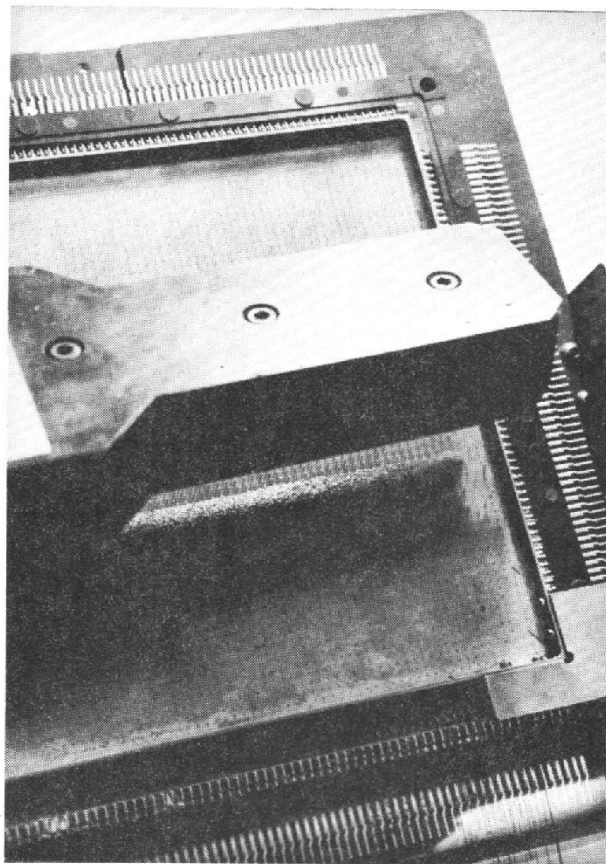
La mémoire à aiguilles est fabriquée entièrement automatiquement. L'utilisation d'un champ magnétique permet à des milliers d'aiguilles de se dresser sur la pointe et de « marcher » sur le plan de mémoire. Les aiguilles viennent se planter au fur et à mesure dans chacun des trous du plan de mémoire. (Document NCR.)
